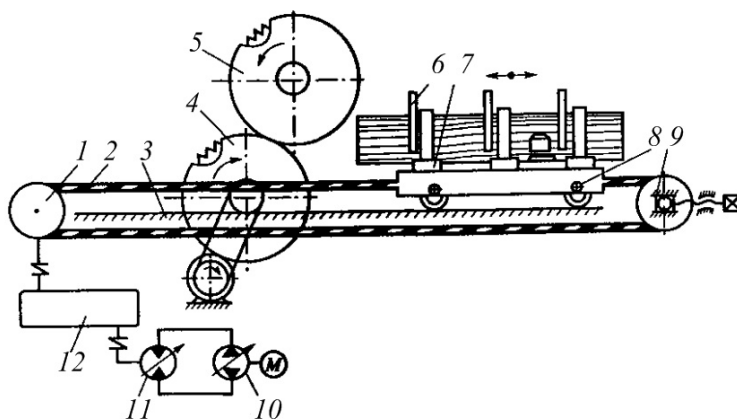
Схема бревнопильного станка ЦДТ-7
